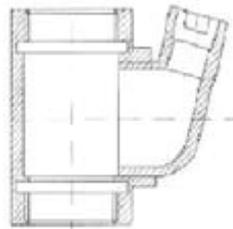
Raccordo di bloccaggio tipo GZ, installato sul tubo verticale
